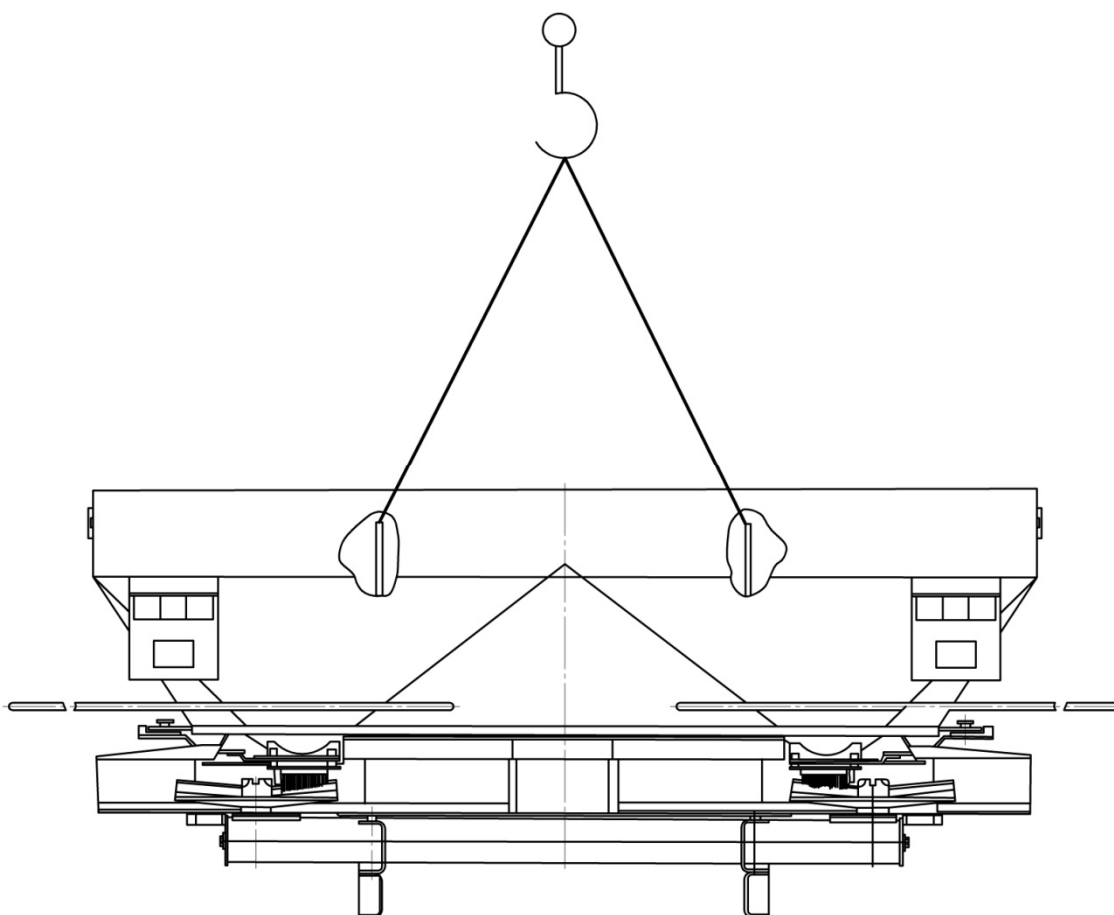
Схема строповки распределителя РУ-1000 и РУ-1600
